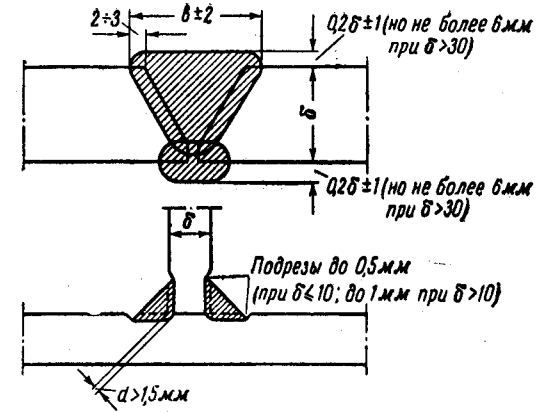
Допуски на размеры швов, выполненных ручной сваркой.
